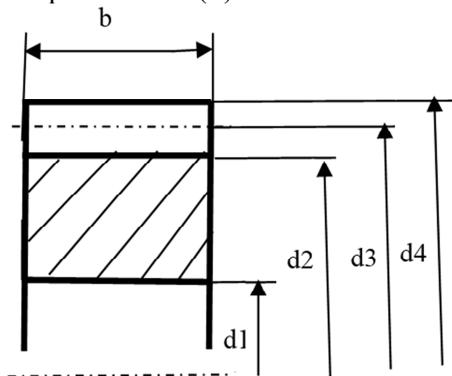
Кодировочная схема шестерни с нанесением размеров
